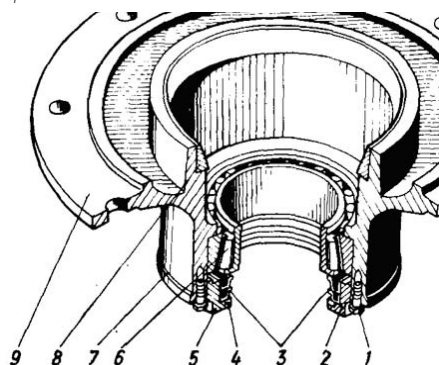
Разборка картера: 1 — болт; 2 — шайба; 3 — манжета; 4 — кольцо; 5 — крышка; 6 — подшипник; 7 — прокладка; 8 — обойма наружная подшипника; 9 — картер
